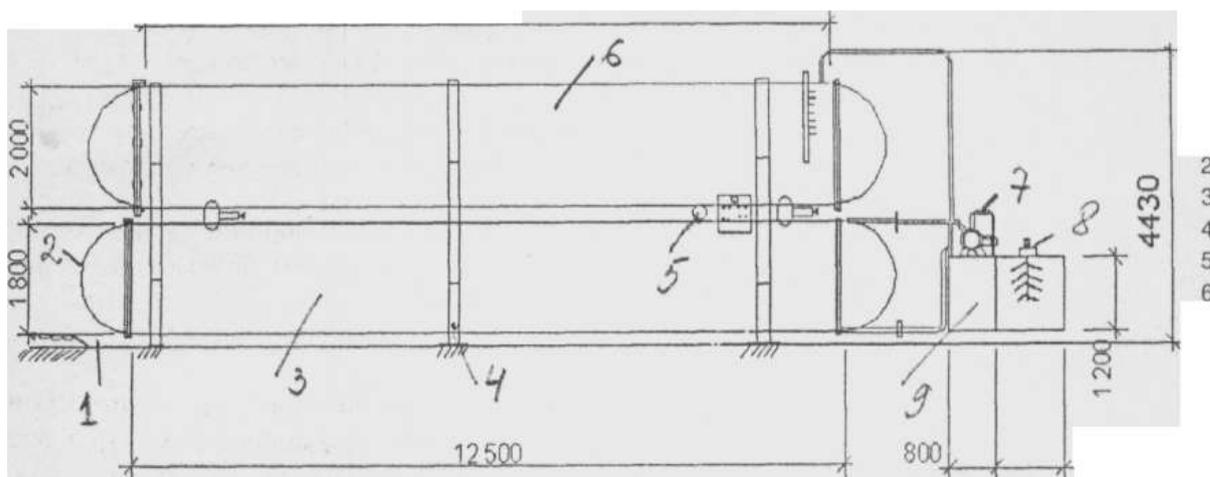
Схема модульной автоклавной установки ЦНИИМОД для глубокой пропитки древесины защитными препаратами: 1 – наружный путь; 2 – крышка; 3 – автоклав; 4 – опора; 5 – манометр; 6 – резервная емкость; 7 – насос высокого давления; 8 – мешалка; 9 – емкость для воды
